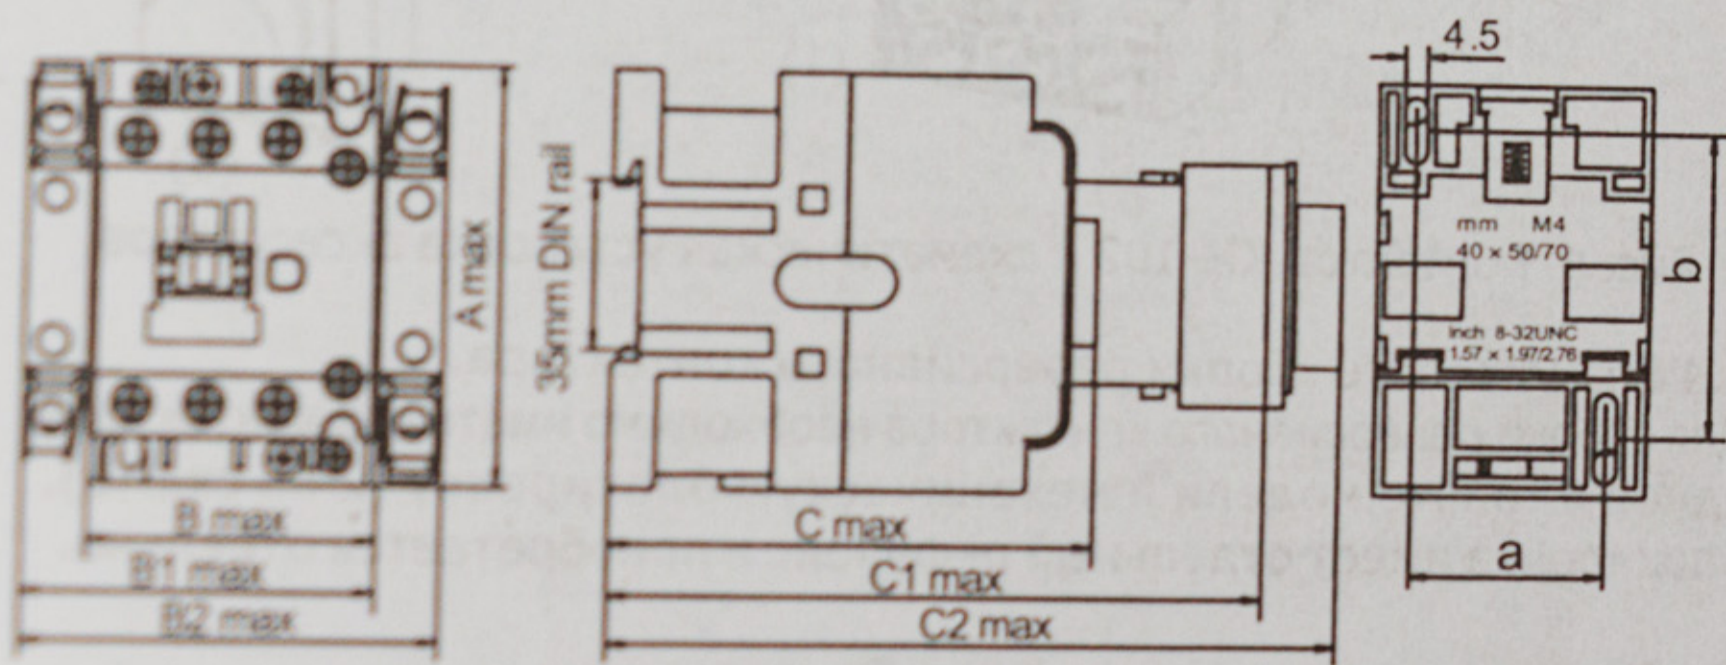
Габаритные и установочные размеры контакторов на токи 6А–38А, мм.
